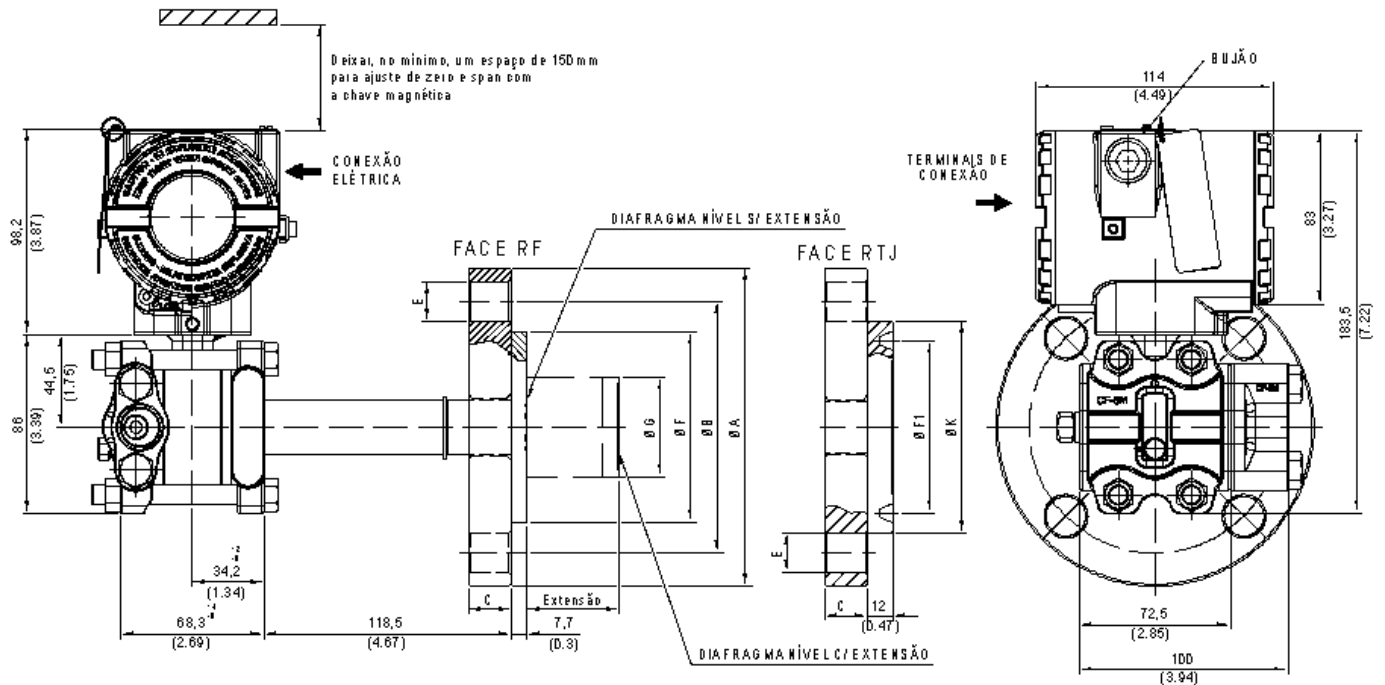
(a) - Desenho Dimensional de Montagem – Transmissor de Pressão Diferencial, Manométrica, Absoluta, Vazão, Alta Pressão Estática com Suporte
